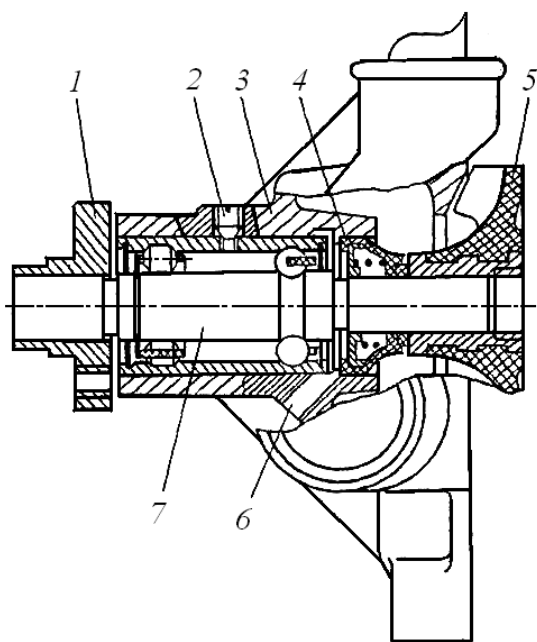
Водяной насос: 1 – ступица; 2 – фиксатор; 3 – корпус; 4 – сальник; 5 – крыльчатка; 6 – контрольное отверстие для выхода охлаждающей жидкости; 7 – валик с подшипником
